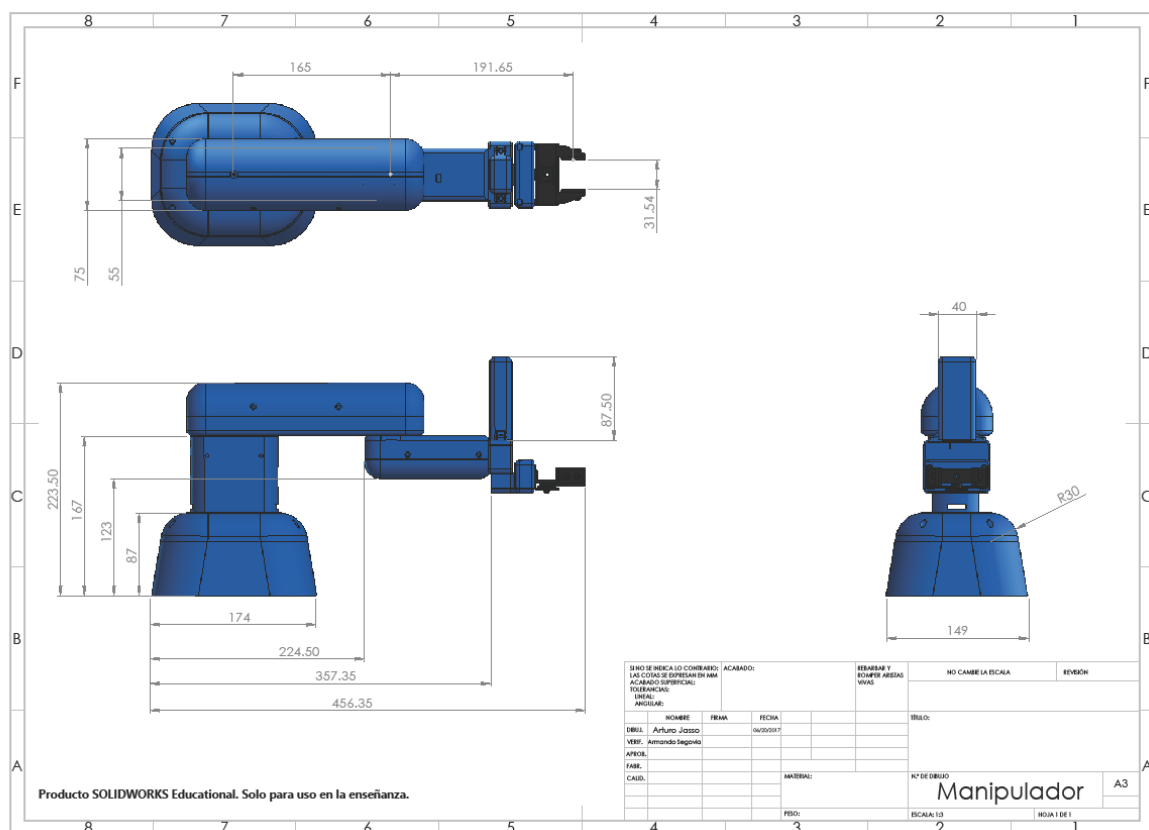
Dibujo en SolidWorks® del ensamblaje del manipulador final
